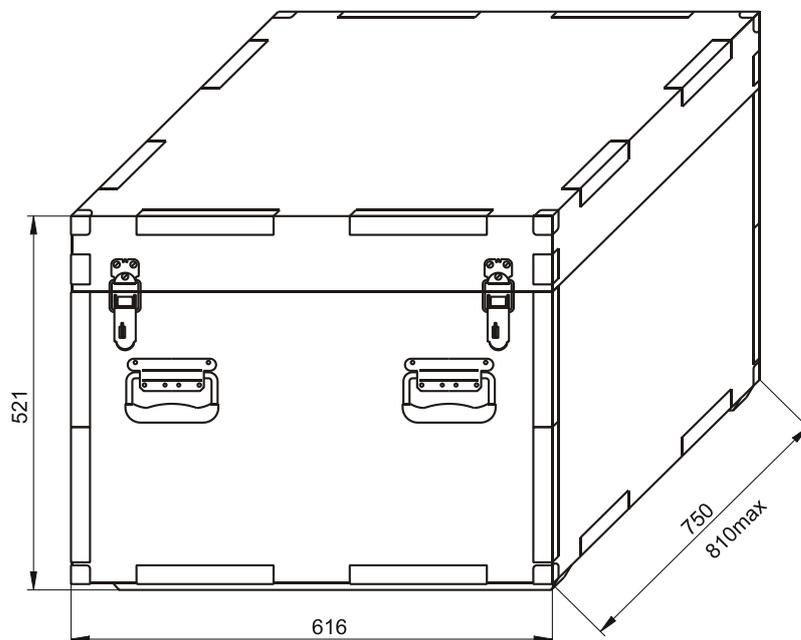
Габаритные размеры ящика укладочного ЯКУР.323361.017
